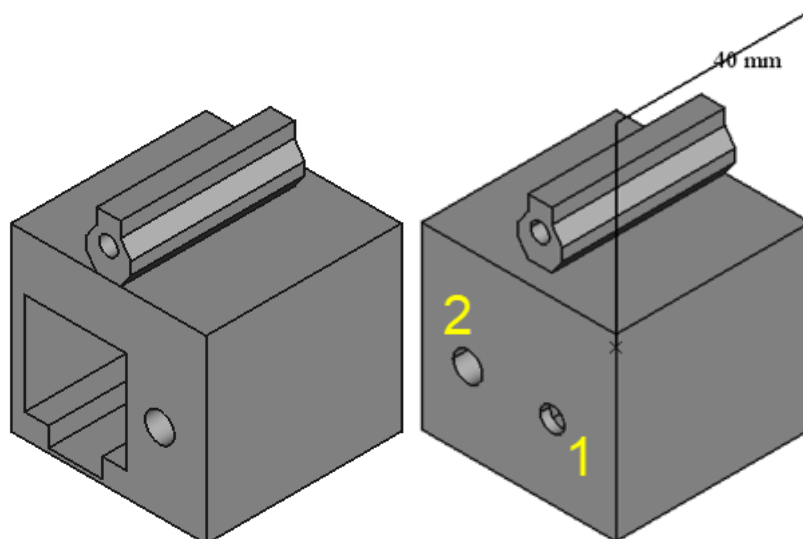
Vista axonométrica frontal y trasera de la caja del motor
